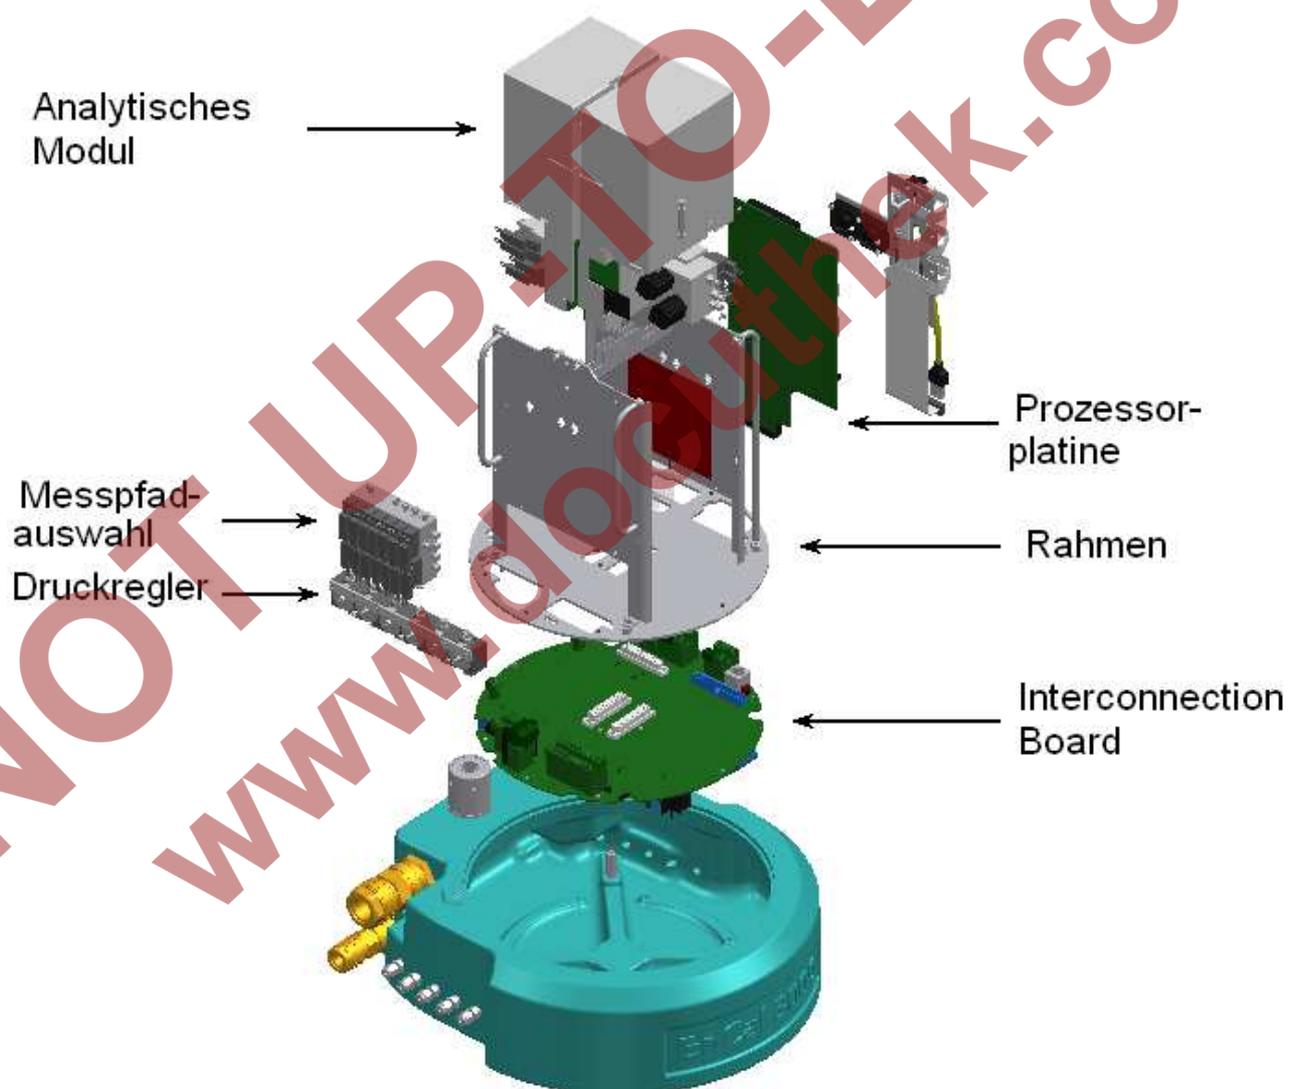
Explosionsdarstellung der internen Bauteile des EnCal 3000 Quad
